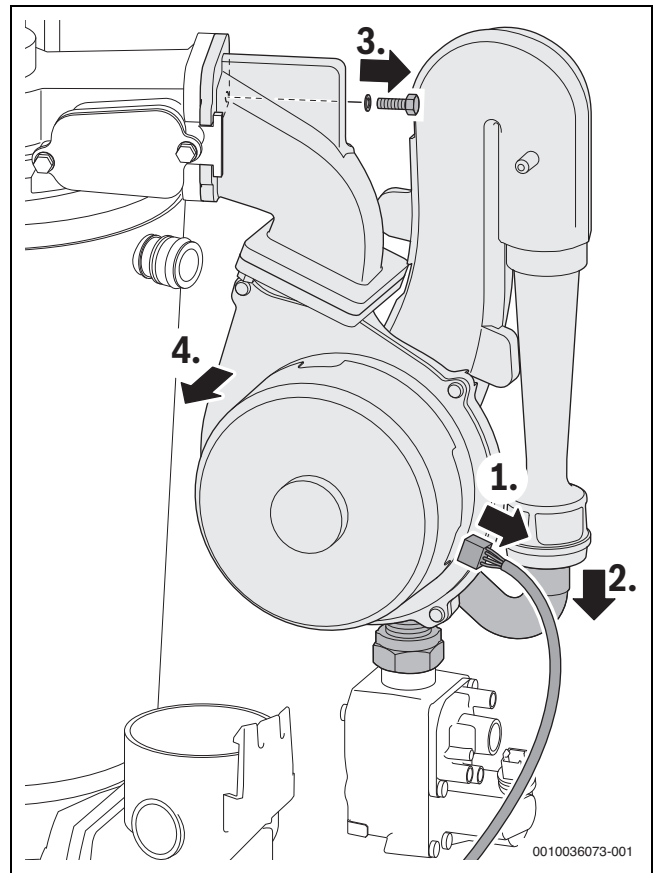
Desmontar o ventilador com dispositivo de mistura
